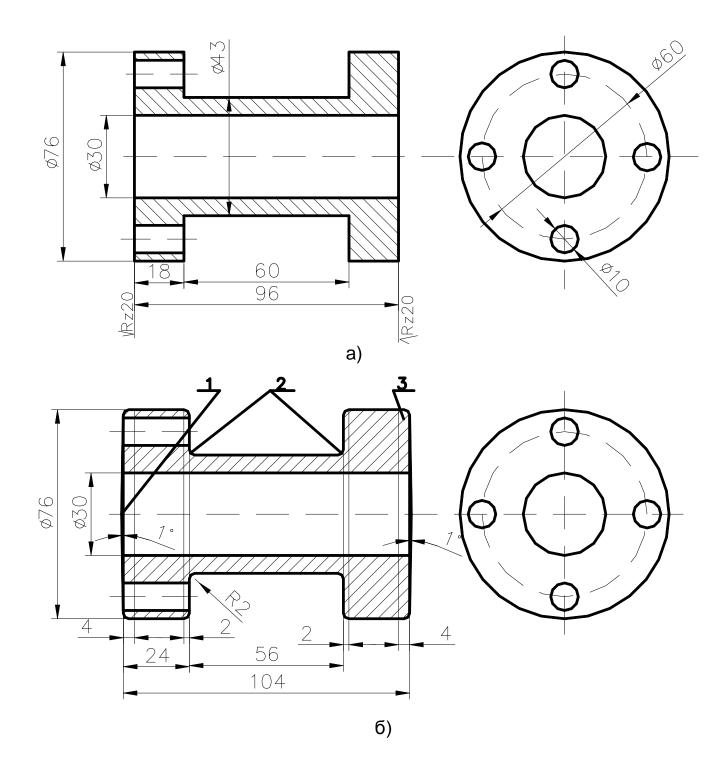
Чертеж детали «Втулка» (а) и чертеж отливки (б): 1 – литейный уклон, 2 – литейный радиус, 3 – припуск на обработку.
